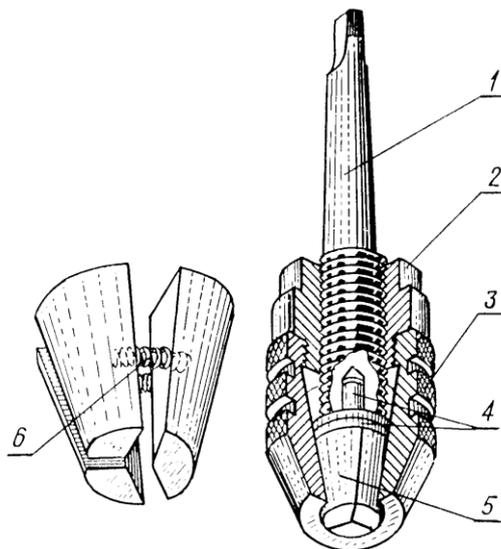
Способы крепление инструмента в шпинделе сверлильного станка
